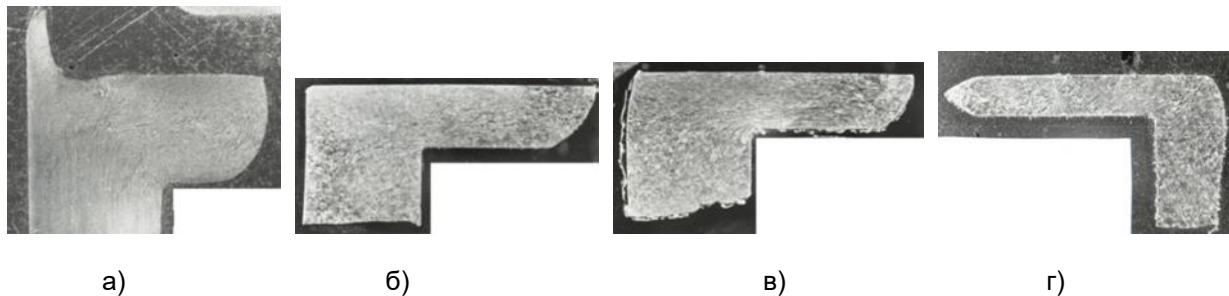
Перерізи зовнішніх фланців на трубних заготовках при різних положеннях валка і відносних розмірах виставленої під деформування частини заготовки
